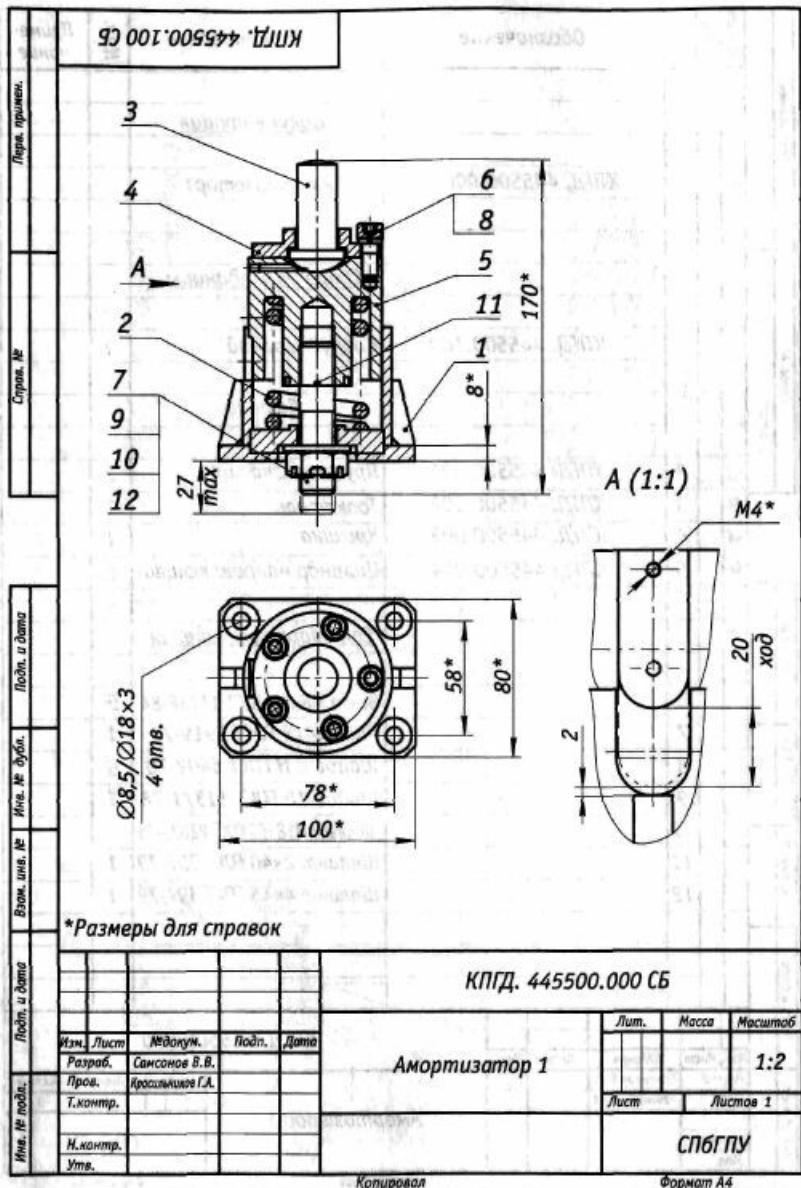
Сборочный чертеж «Амортизатор 1»
